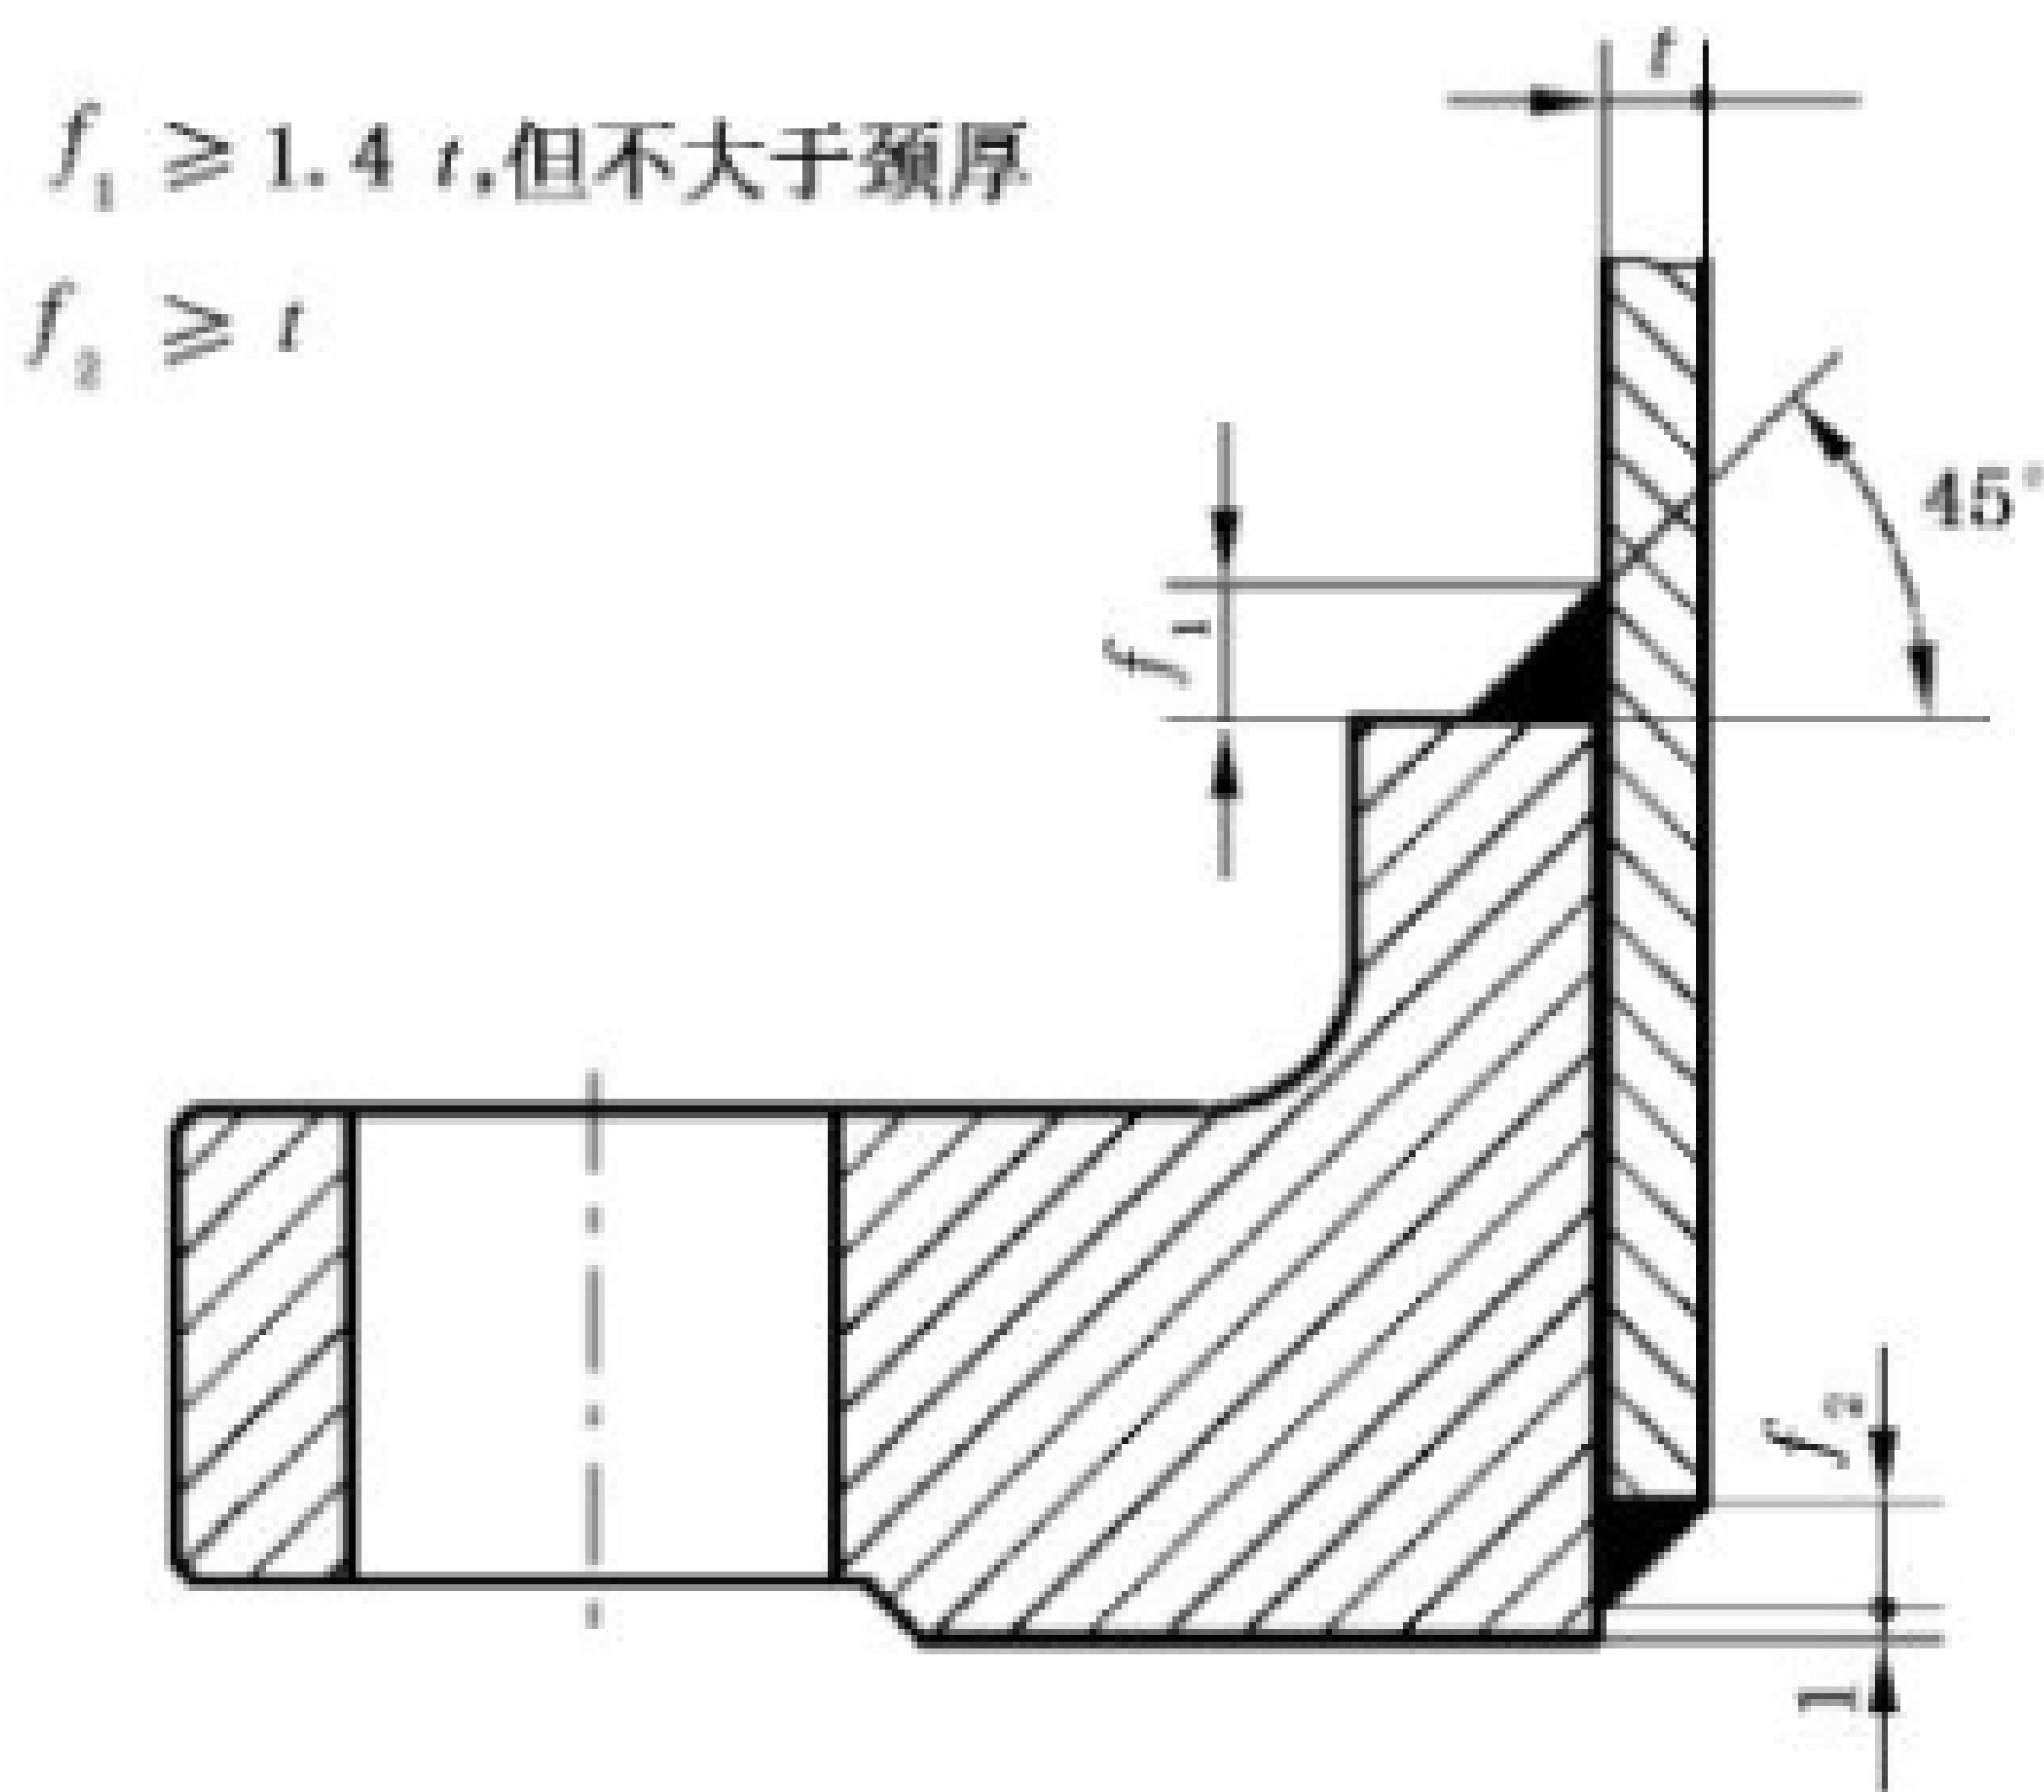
带颈平焊法兰与钢管的焊接连接
